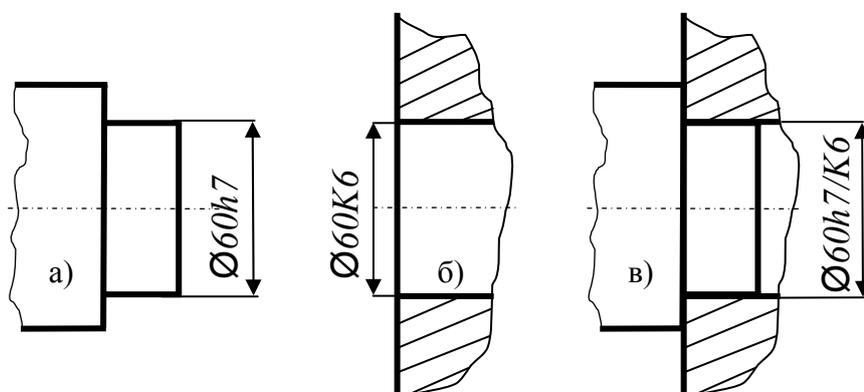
Допуск вала, допуск отверстия и сопряжение вала с отверстием. Посадка переходная. Система вала.
